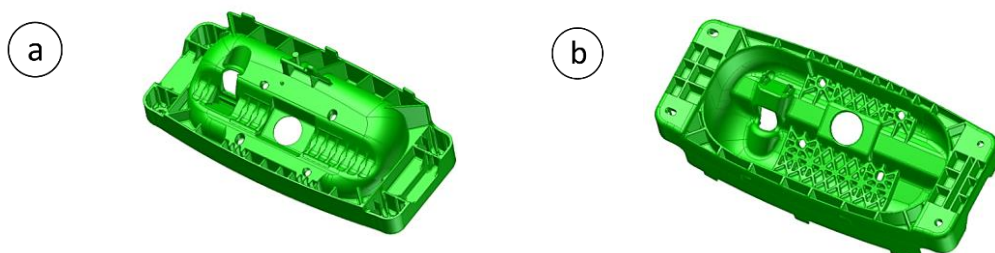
Airbaggehäuse a) Außenansicht, b) Innenansicht
